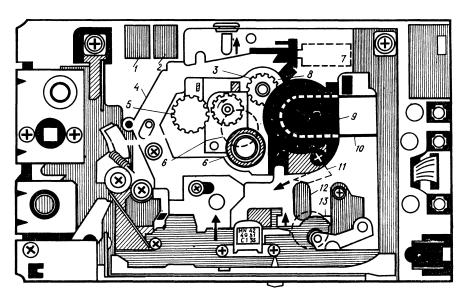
Внешний вид ЛПМ: 1 — рычаг предотвращения записи; 2 — рычаг определения наличия кассеты; 3 — узел муфты (зубчатое колесо); 4 — рычаг тормоза, 5 — подающая катушка; 6 — направляющий ролик; 7 — сердечник тормоза; 8 — передающее зубчатое колесо, 9 — приемная катушка, 10 — пассик; 11 — стопорная пластина вспомогательного основания; 12 — тонвал (маховик); 13 — прижимной ролик
